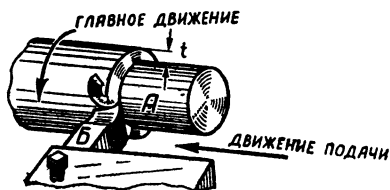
Схема снятия стружки на токарно-винторезном станке.
